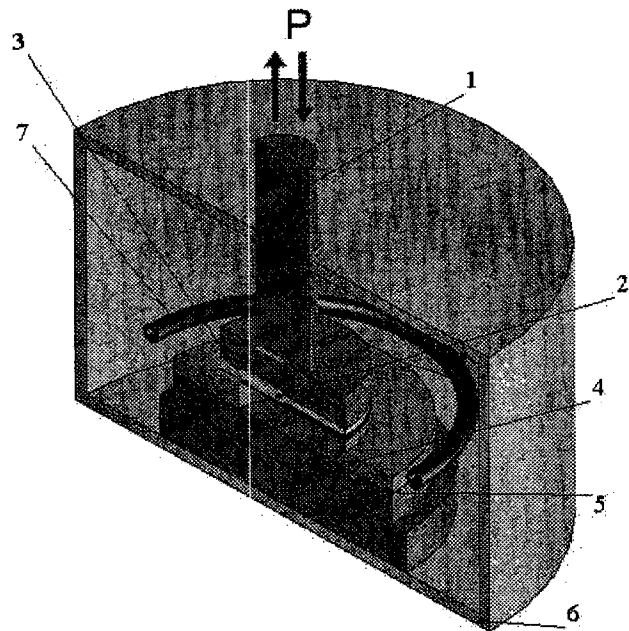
Схема осуществления диффузионной сварки фланца с фольгой
